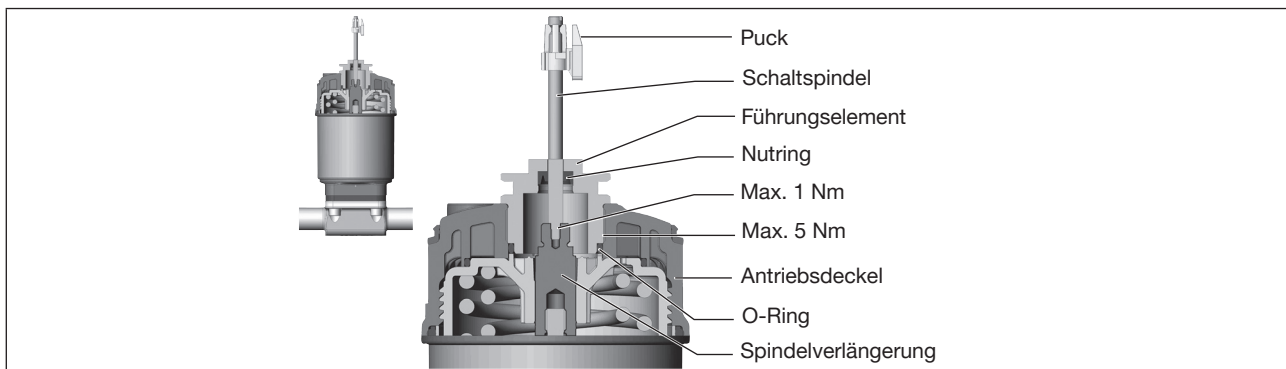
Schaltspindel montieren (2), integrierte Steuerluftführung
